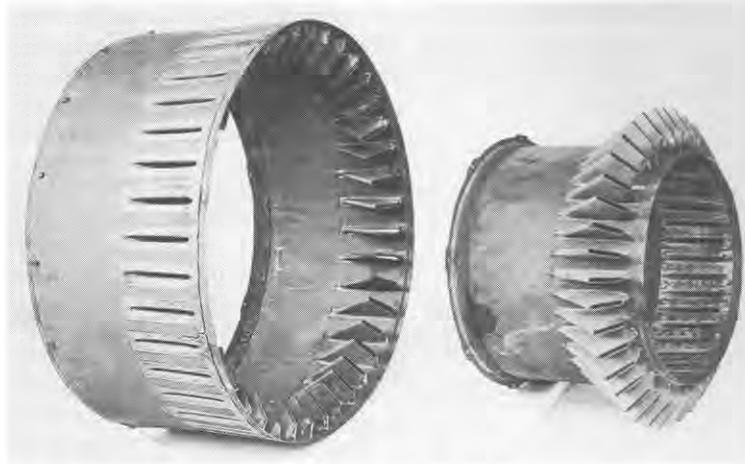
Камера сгорания турбореактивного двигателя БМВ 109-003 А-1. Обратите внимание на полые пальцы, выступающие из каждой секции для подачи вторичного воздуха
